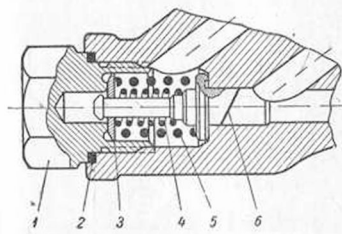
Рабочий клапан хода сжатия: 1—пробка; 2—алюминиевая шайба; 3—шайба стержня клапана; 4—внутренняя пружина; 5—наружная пружина; 6—ствержень клапана.
